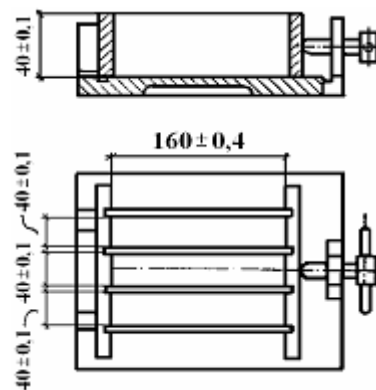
Форма для виготовлення розчинних зразків-балочок
